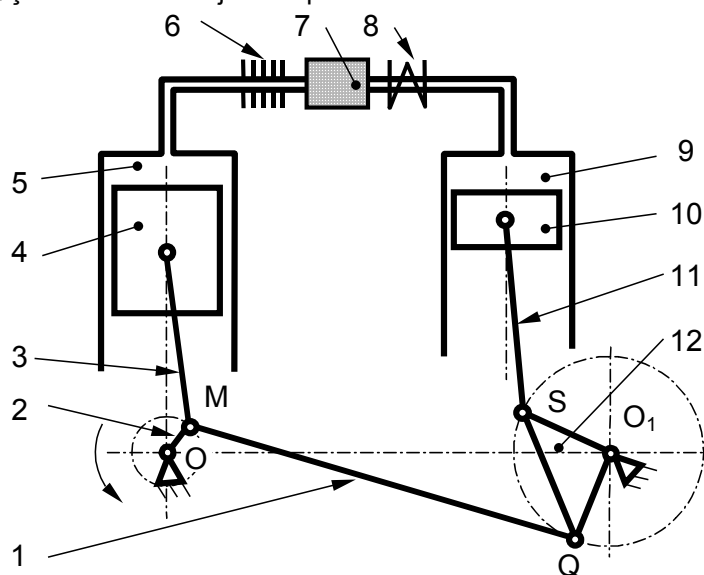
Motor Stirling de tip „alfa“ cu mecanism manivelă - bielă - balansier de tip Ross „Rocker - V“: 1 - tijă; 2 - arbore cotit; 3 - biela pistonului împingător; 4 - piston împingător; 5 - cameră de destindere; 6 - încălzitor; 7 - regeneratoare; 8 - răcitor; 9 - cameră de comprimare; 10 - piston motor; 11 - biela pistonului motor; 12 - balansier
